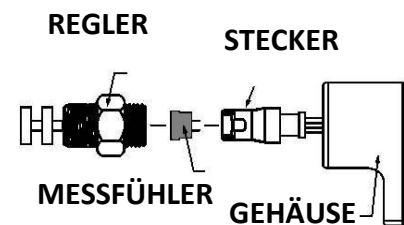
Explosionszeichnung eines Klasse I, Gruppe D Thermostats mit Messfühler (Ersatzteil).
